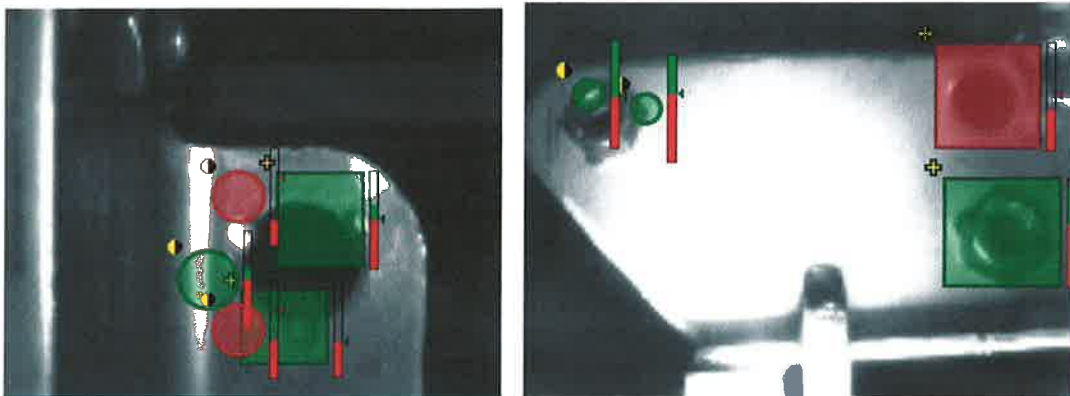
a) Falta de tuerca M14 en pieza izquierda. b) Falta de una tuerca M12 en pieza izquierda.
